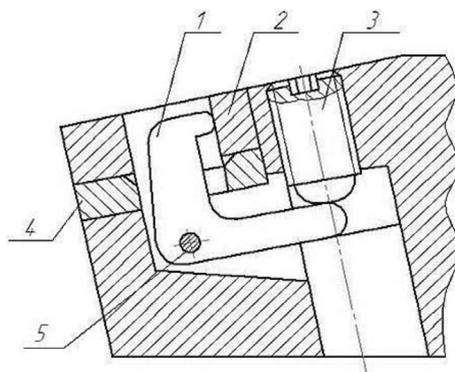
Крепление режущей пластины с помощью поворотного рычага
